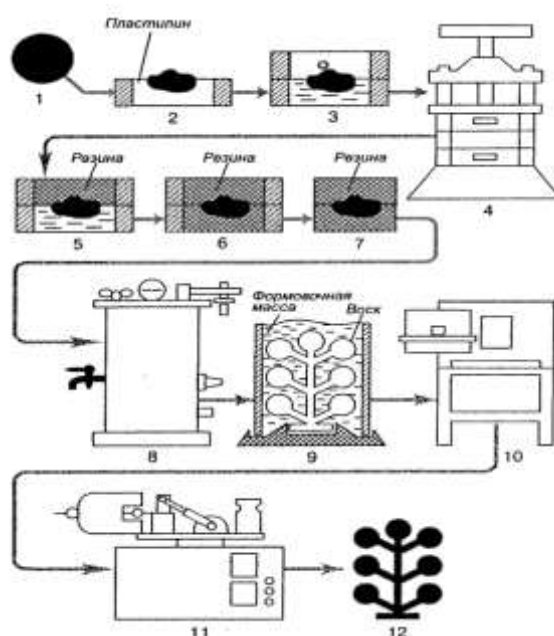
Блок – схема технологического процесса изготовления ювелирных изделий методом литья: 1 – сырая резиновая смесь; 2,3 – подготовка резиновой смеси; 4 – прессование резиновой смеси на вулканизационном прессе; 5 – охлаждение обжимки с резиновой смесью в воде; 6 – разрезание резиновой пресс-формы; 7 – вынимание из резиновой пресс-формы модели (эталона изделия); 8 – изготовление восковой модели в резиновой пресс-форме; 9 – сборка моделей в блоки, образование блок-куста; 10 – вибровакuumирование; 11 – выпаривание воскового состава в печах; 12 – отделение отливок от литниковой системы.
